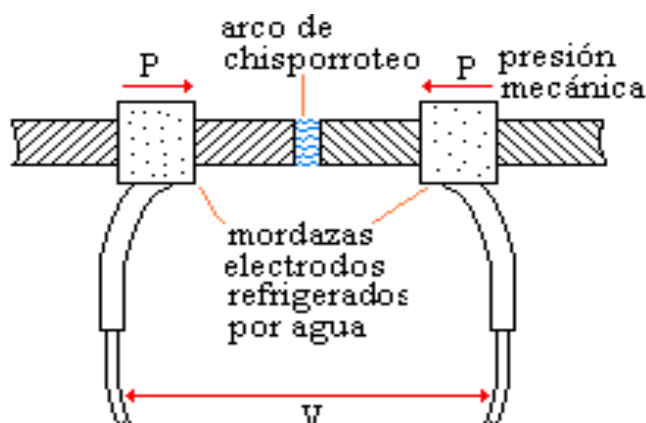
Soldadura por resistencia de chispa
